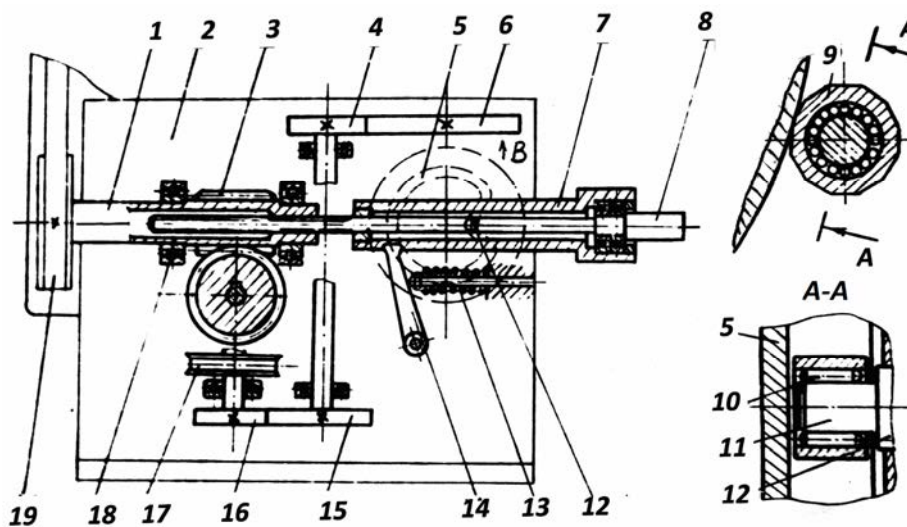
Передаточний механізм привода плоскокулачкової силової головки для подрібнення зливної стружки
